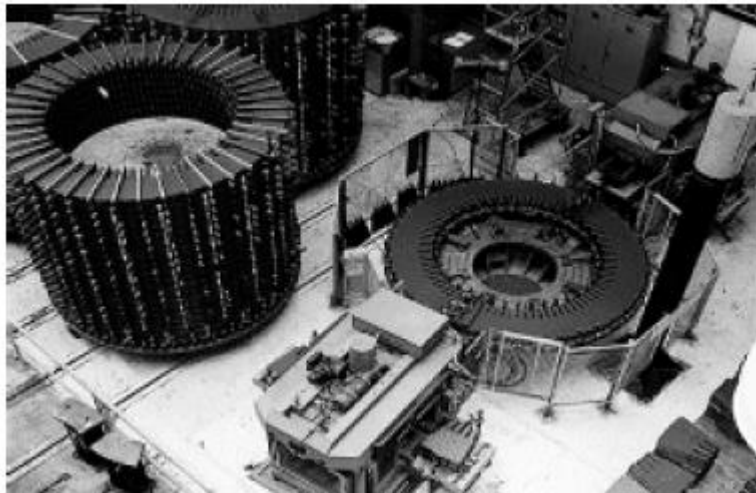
Assemblage des tôles d'un stator de turboalternateur [51]
